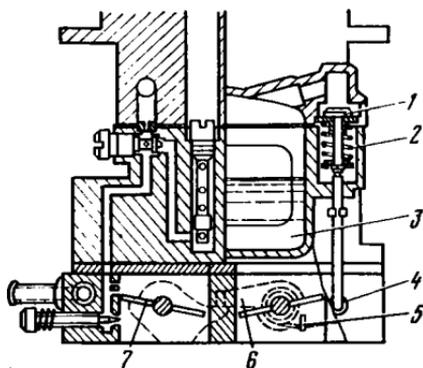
Устройство механизма разбалансировки поплавковой камеры
